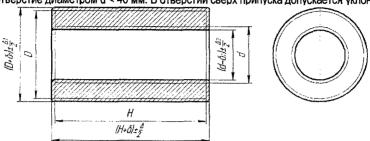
Схема назначения припусков для поковок 4-ой группы
